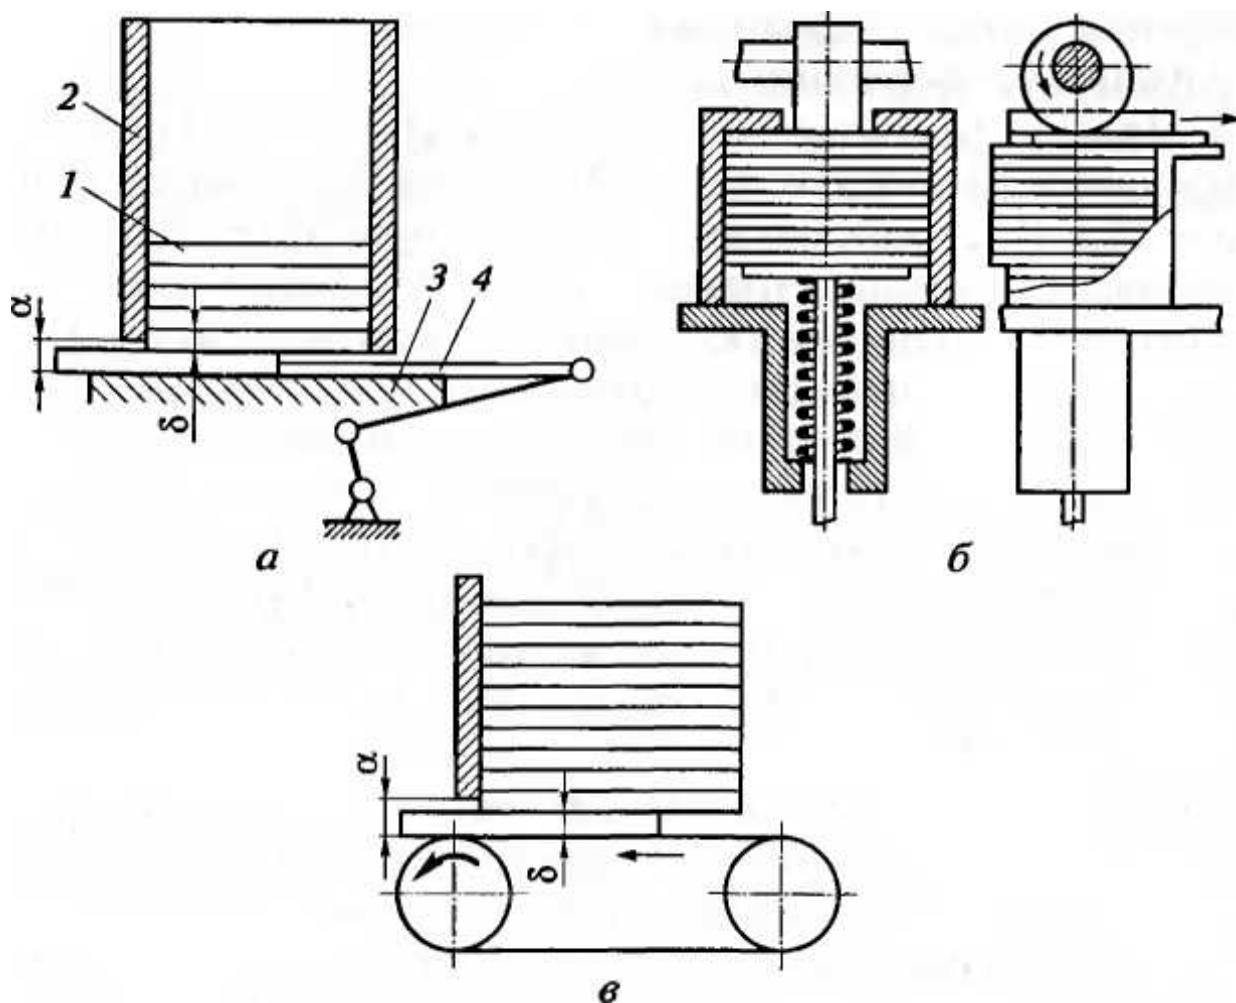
Пристрої для подачі деталей у зону обробки: а – шибєрні: 1 – деталі; 2 – стінка; 3 – майданчик; 4 – штовхач; б, в – фрикційні [6]
